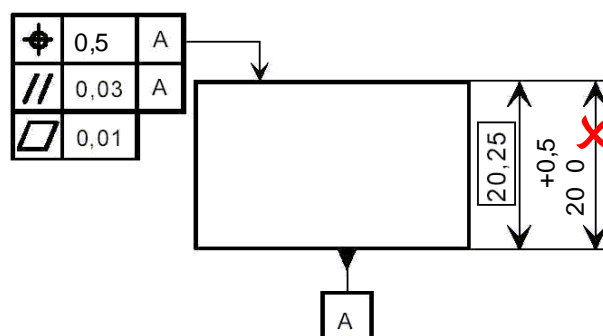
Relações entre especificações dimensionais e geométricas. Adaptada de [S1]
